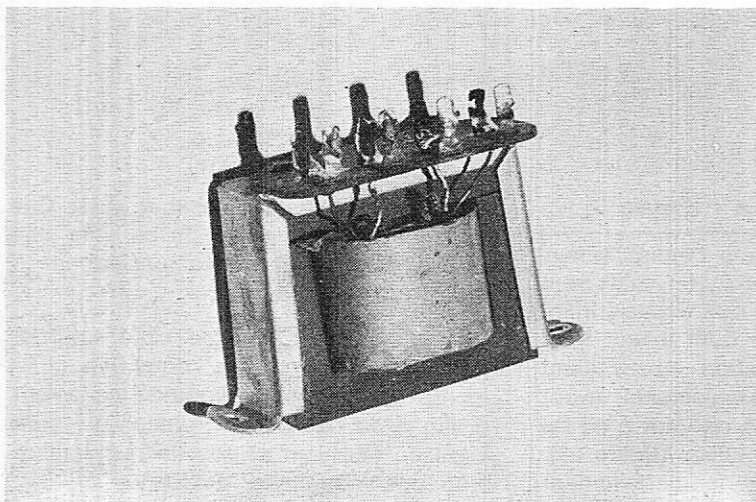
Le transformateur avant démontage. La première opération consiste à dessouder ou couper les connexions de sortie.
